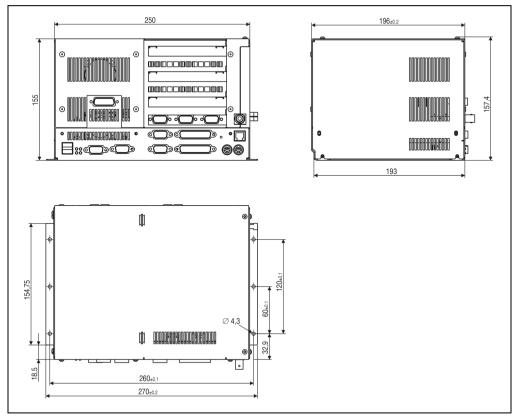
Dimensions IPC5000 / IPC5000C (4 emplacements)
